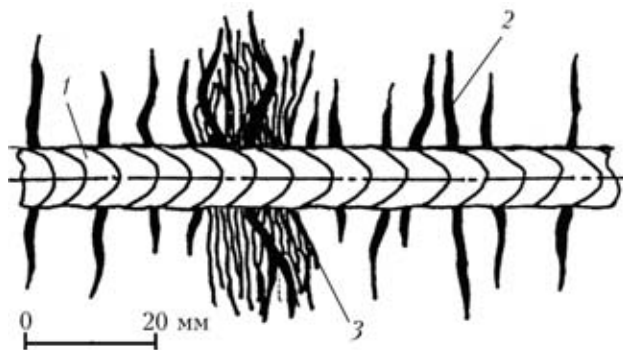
Картины ПЧЛ, полученных на образцах стыкового соединения стали Ст3: 1 — шов; 2 — прилегающая к шву зона после сварки; 3 — то же + ЭДО
